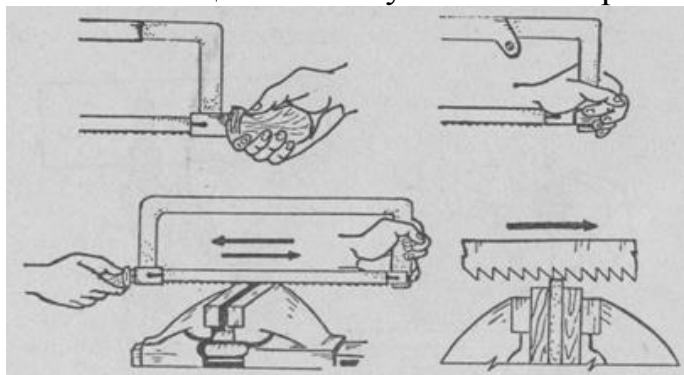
Приемы работы с ножовкой по металлу и слесарными ножницами
